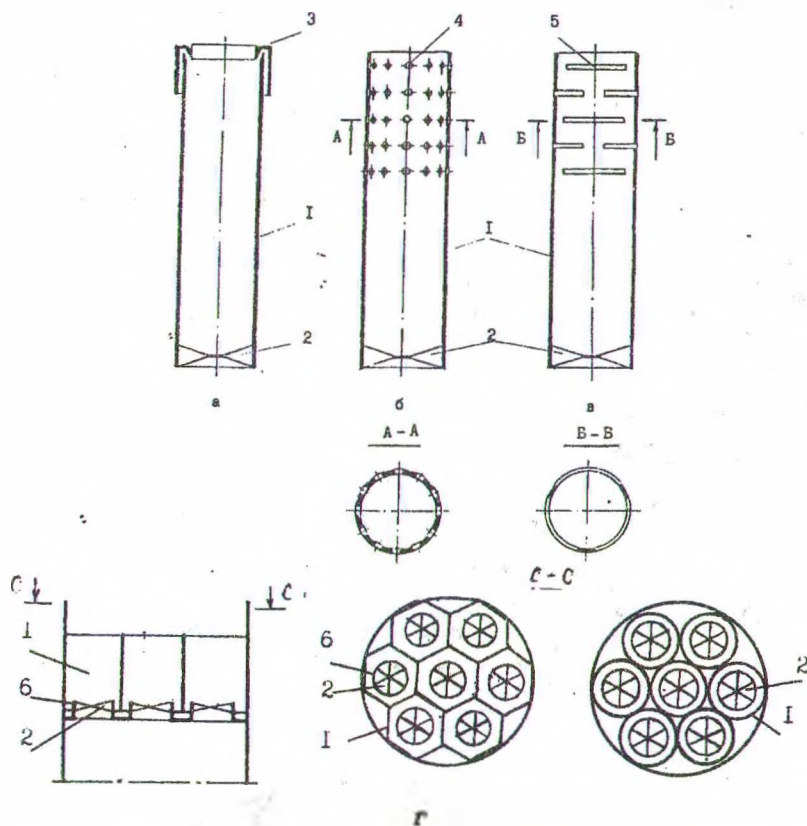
Центробежные сепарационные устройства: а – с отбойным колпачком; б – с круглыми отверстиями; в – со щелями; г – с противоточным отводом жидкости; 1 – цилиндрический (или шестигранный) патрубок; 2 – завихритель; 3 – отбойный колпачок; 4 – отверстия; 5 – щели; 6 – стакан
